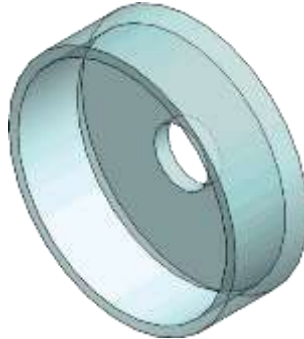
Tapa del motor a pasos basado en fuerza de Lorentz.
